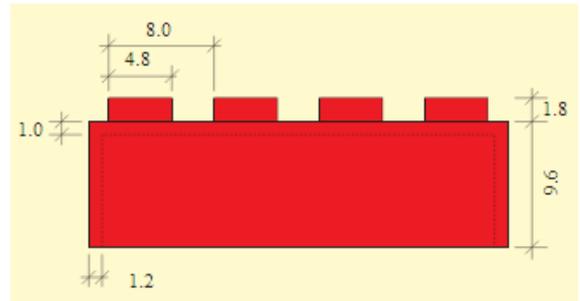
Vista lateral izquierda de una pieza de LEGO 4x2 [6].
